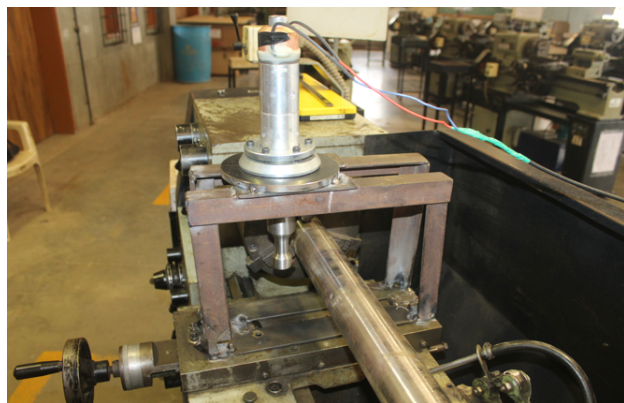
Реальная фотография базовой рамы с закрепленным UVANT
